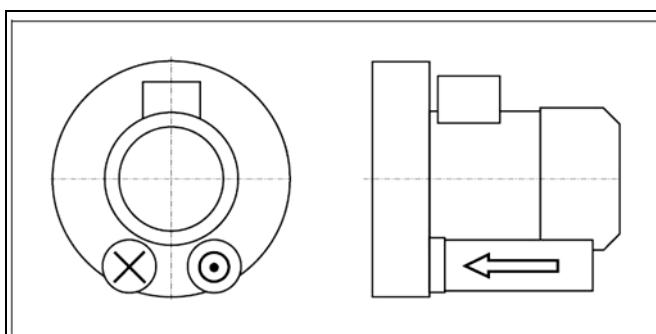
Вакуумный насос/компрессор с одним рабочим колесом.
